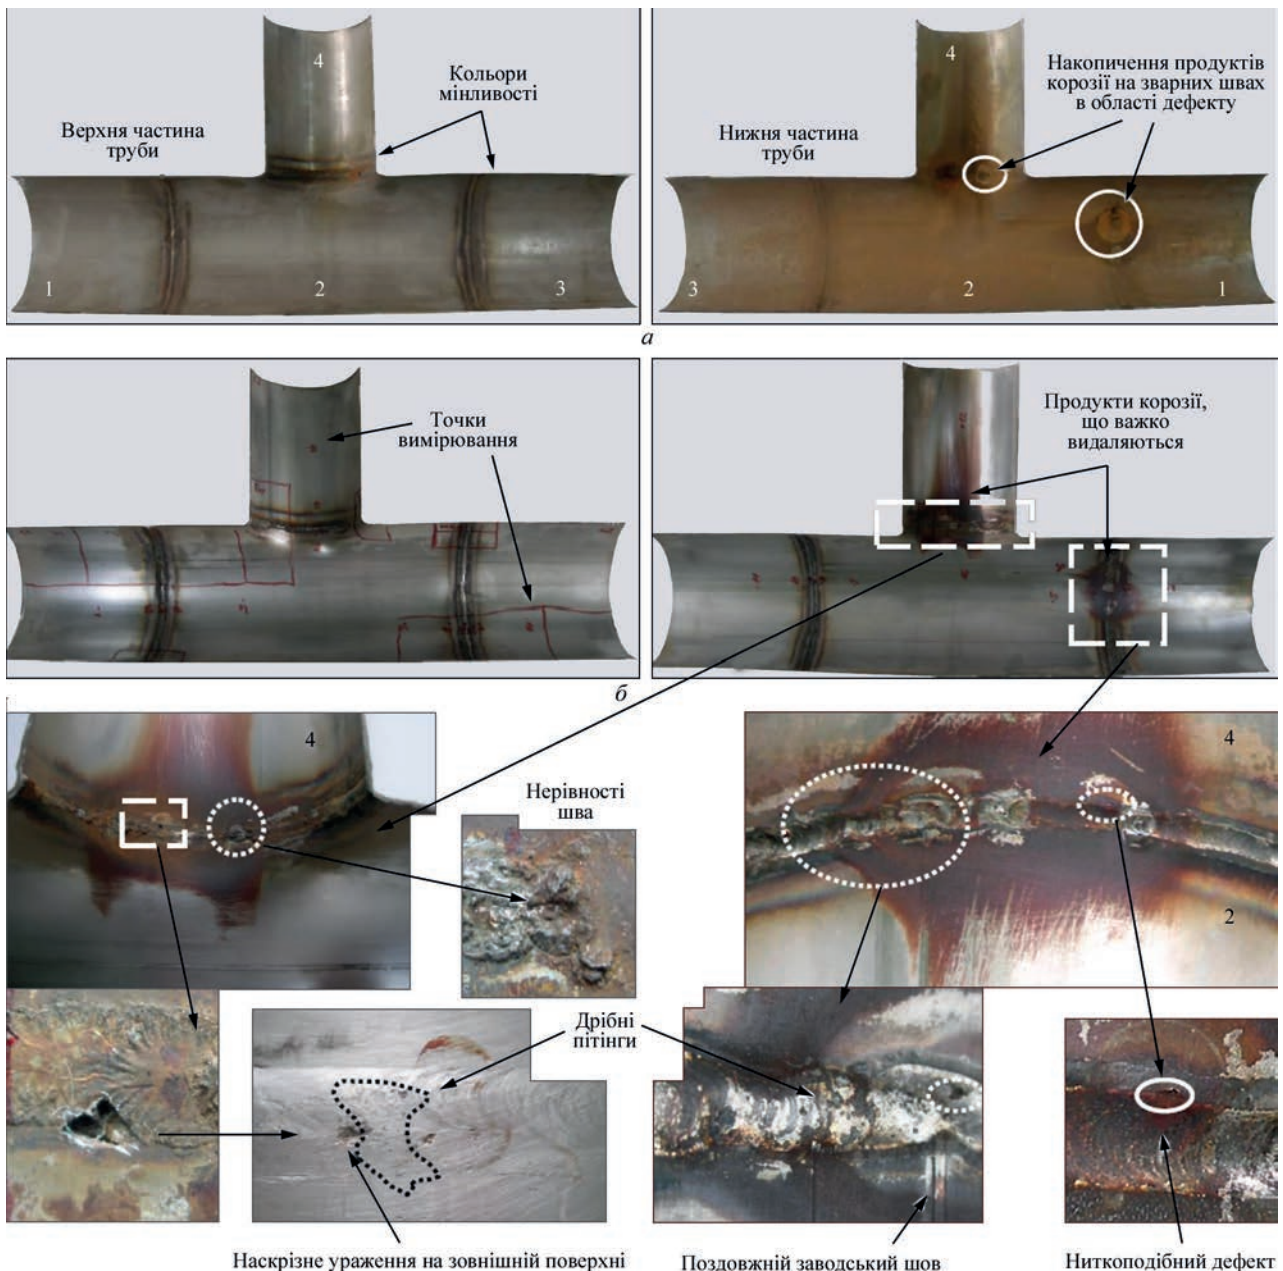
Зовнішній вигляд зразка зварного з'єднання труб № 1–4: а – внутрішня поверхня з продуктами корозії; б – внутрішня поверхня після видалення продуктів корозії; в – дефекти в області швів
